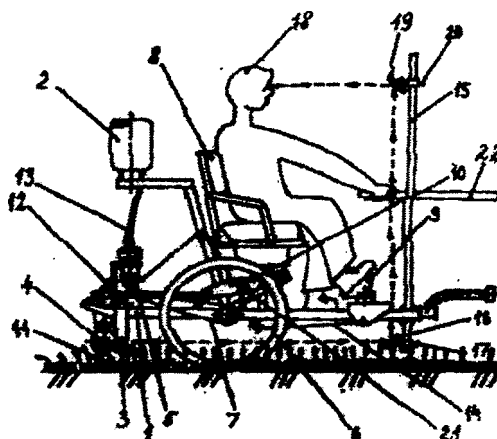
Устройство для контактного уничтожения сорняков раствором гербицида: 1-рама; 2-бачок для рабочего раствора; 3-кронштейн; 4-валец; 5-система подачи рабочего раствора к валцу; 6-опорные колеса; 7-цепная передача привода вальца; 8-сидение; 9-педали установки высоты вальца; 10-система уравнивания усилия педали; 11-лоток для сбора капель гербицида; 12-кран; 13-поплавковая камера; 14-цепь; 15-стойка; 16-нижнее зеркало; 17-винт; 18-оператор; 19-верхнее зеркало; 20-винт регулировки зеркала; 21-палец; 22-мотоблок.
